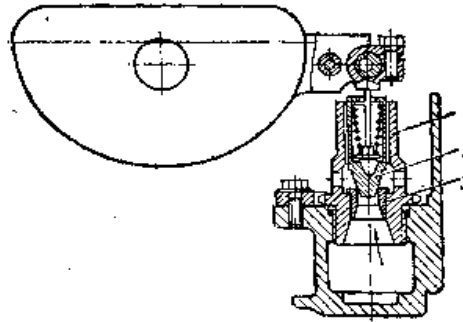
Схема поплавкового механізму карбюратора: 1 - гніздо; 2 - голка; 3 – сідло
